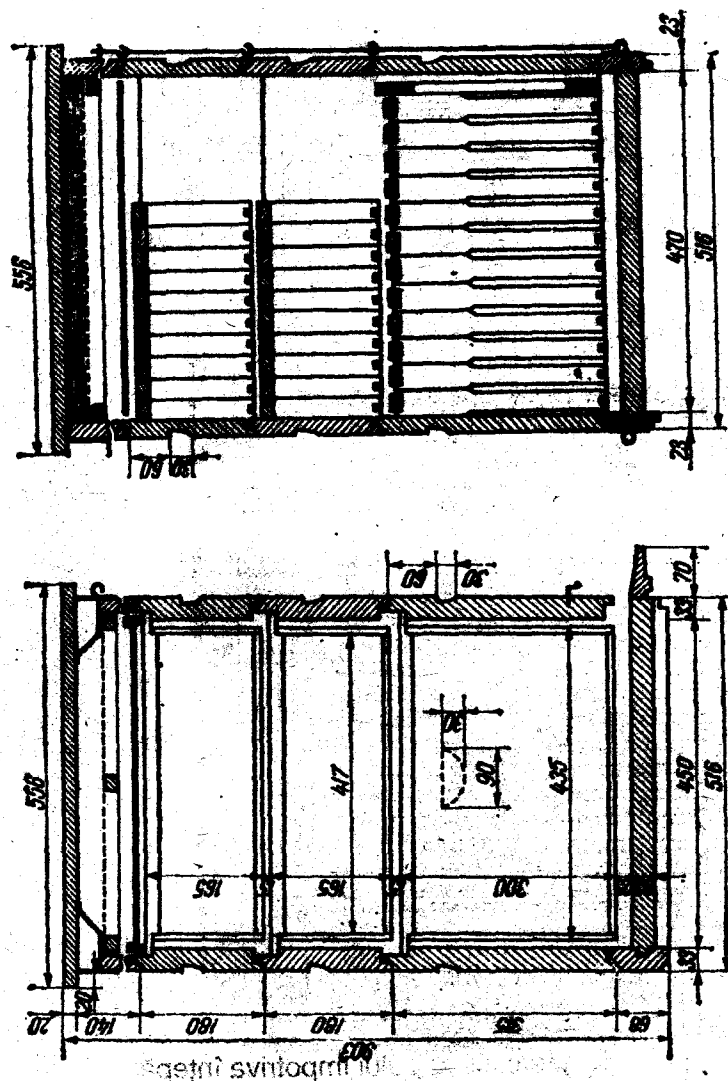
Secțiune longitudinală și transversală în stupul vertical cu magazine
